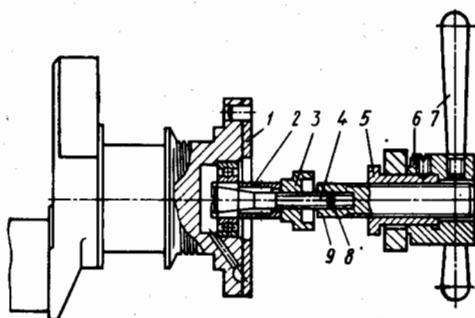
Съемник для выпрессовывания подшипника из коленчатого вала:
